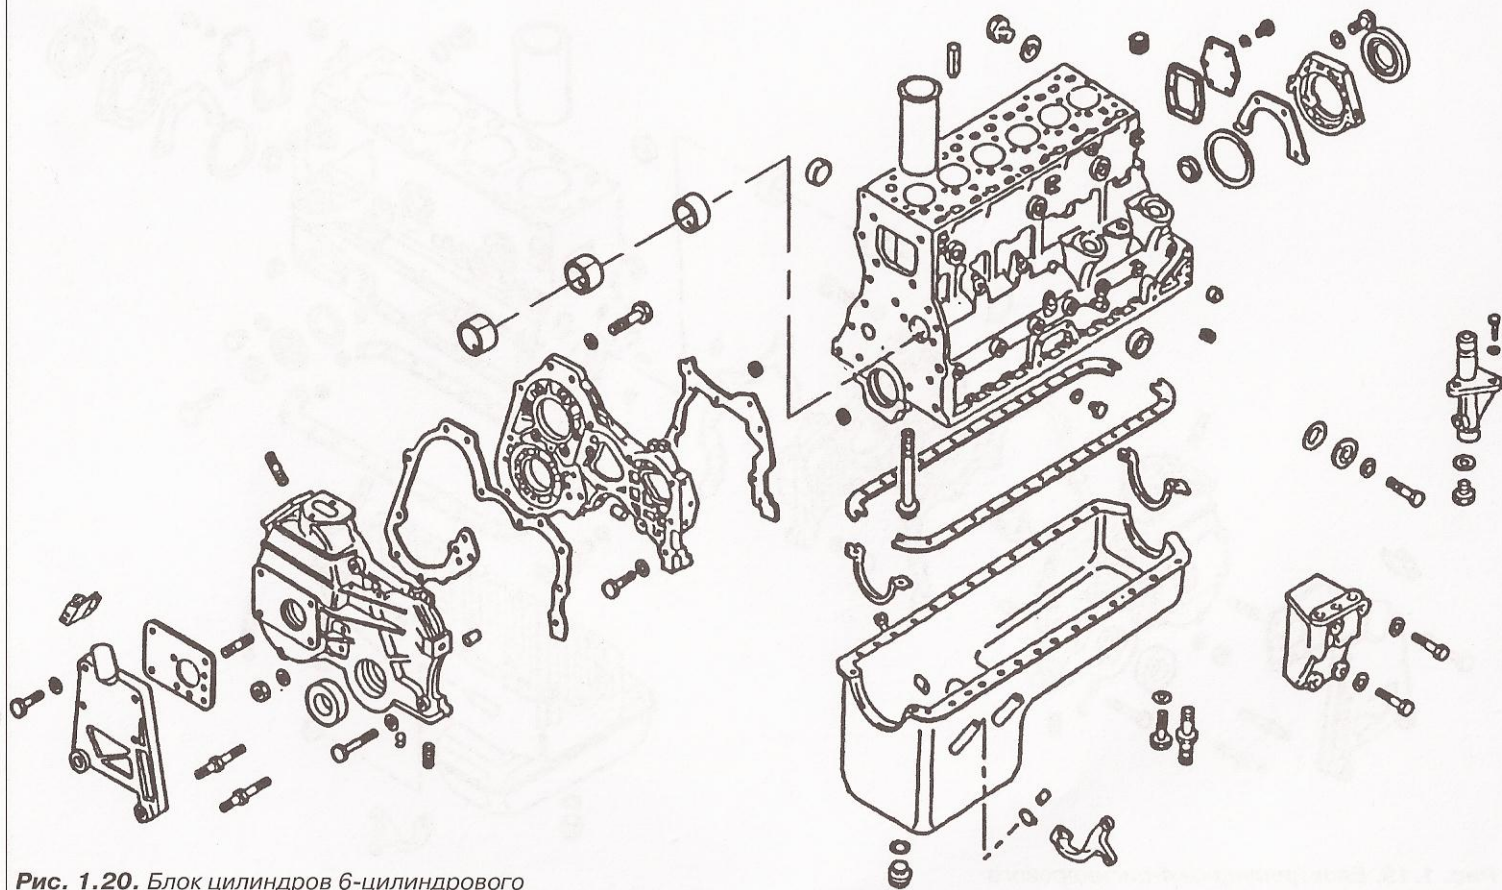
Блок цилиндров 6-цилиндрового двигателя.
